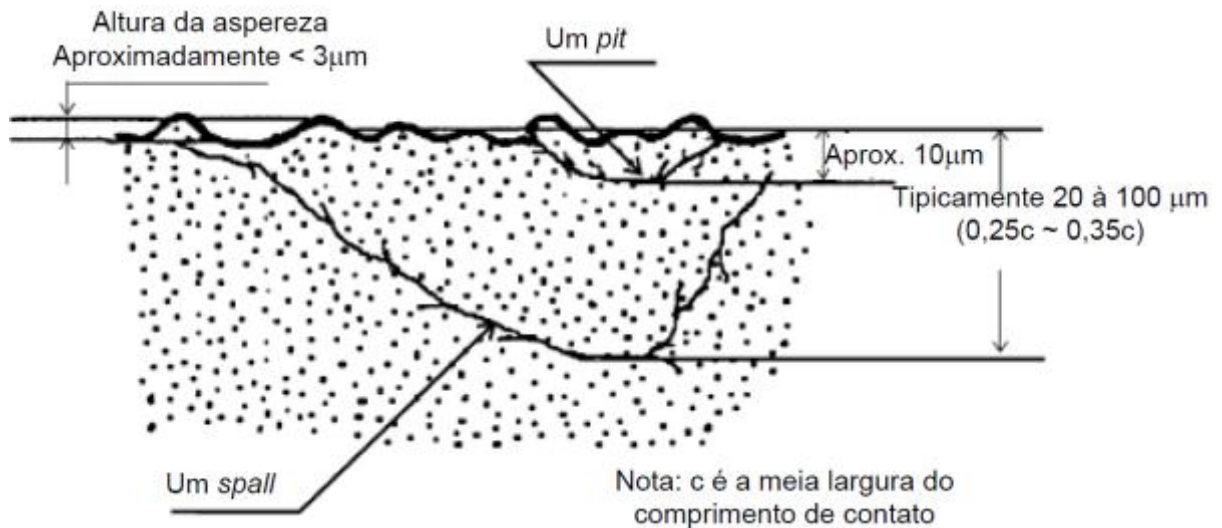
Ilustração esquemática do fenômeno de pitting e spalling (figura modificada, DING e RIEGER, 2003).
